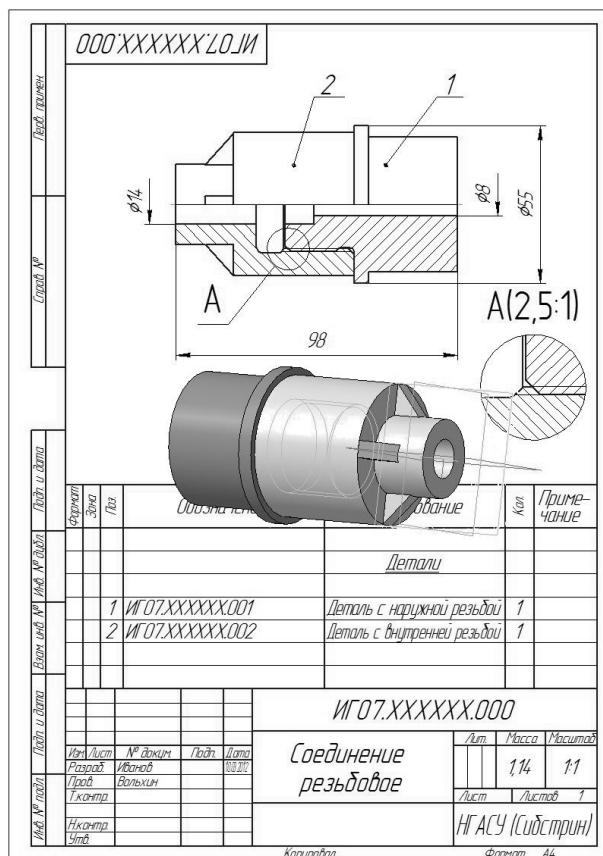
Модель и ассоциативный чертеж резьбового соединения.
